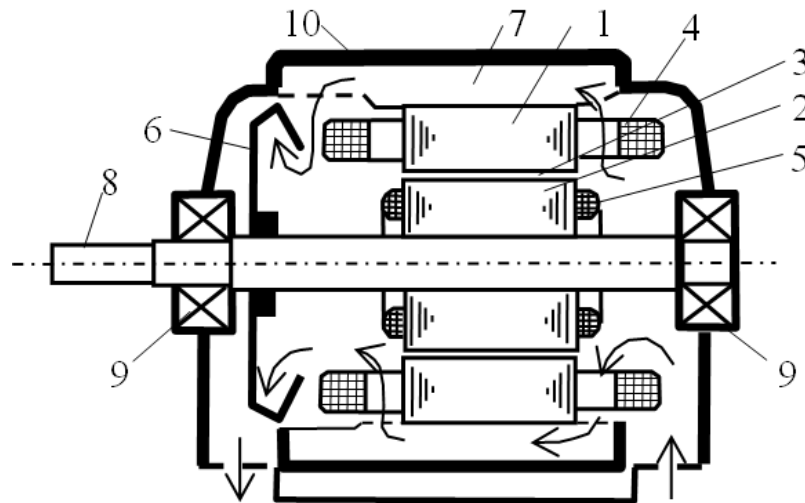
Construction d'un moteur asynchrone : 1 – noyau statorique ; 2 – noyau de rotor ; 3 – entrefer ; 4 – bobinage du stator ; 5 – bobinage du rotor ; 6 – ventilateur ; 7 – les canaux de ventilation (les flèches montrent la direction du mouvement de l'air refroidissant par les canaux) ; 8 – arbre ; 9 – roulements ; 10 – bâti
